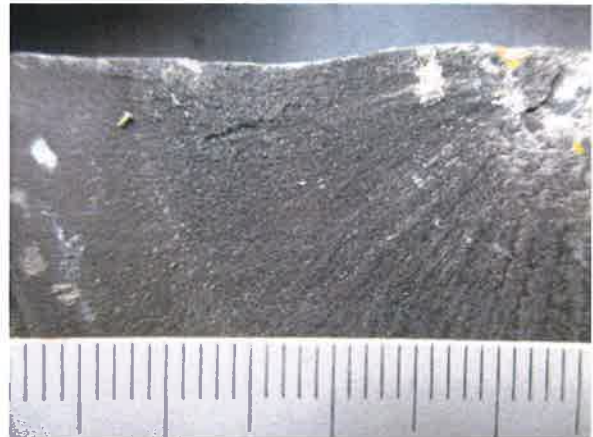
Ansicht Bruchfläche (4) mit starhigen Bruchstrukturen, Bildbreite ca. 35 mm
